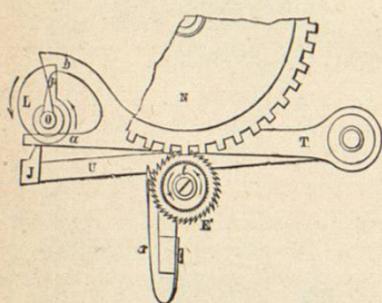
Mecanismo de la impresión en el aparato de Hughes
